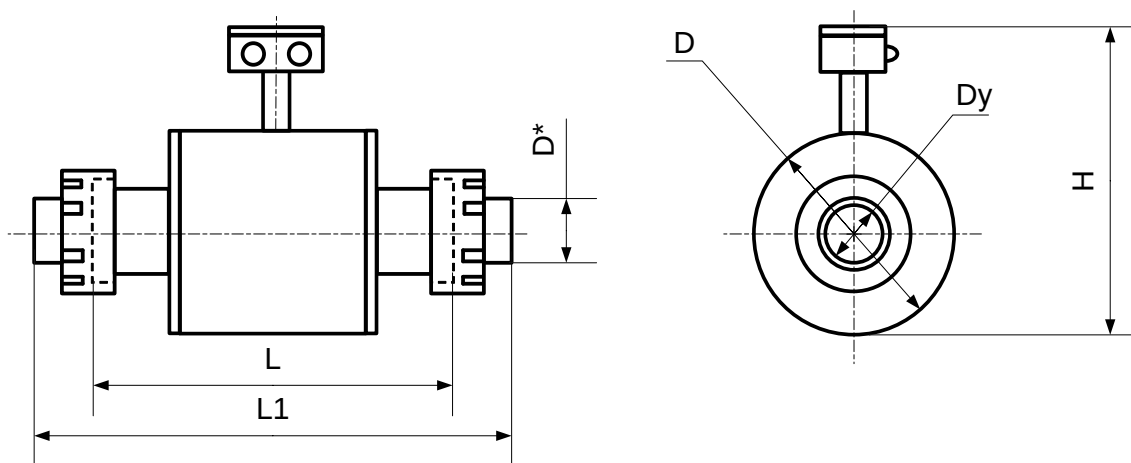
Габаритные, присоединительные размеры и масса резьбовых первичных преобразователей с метрической резьбой Рм, давление измеряемой среды PN до 16 МПа (до 160 Бар) с клеммной коробкой и с разъемом
